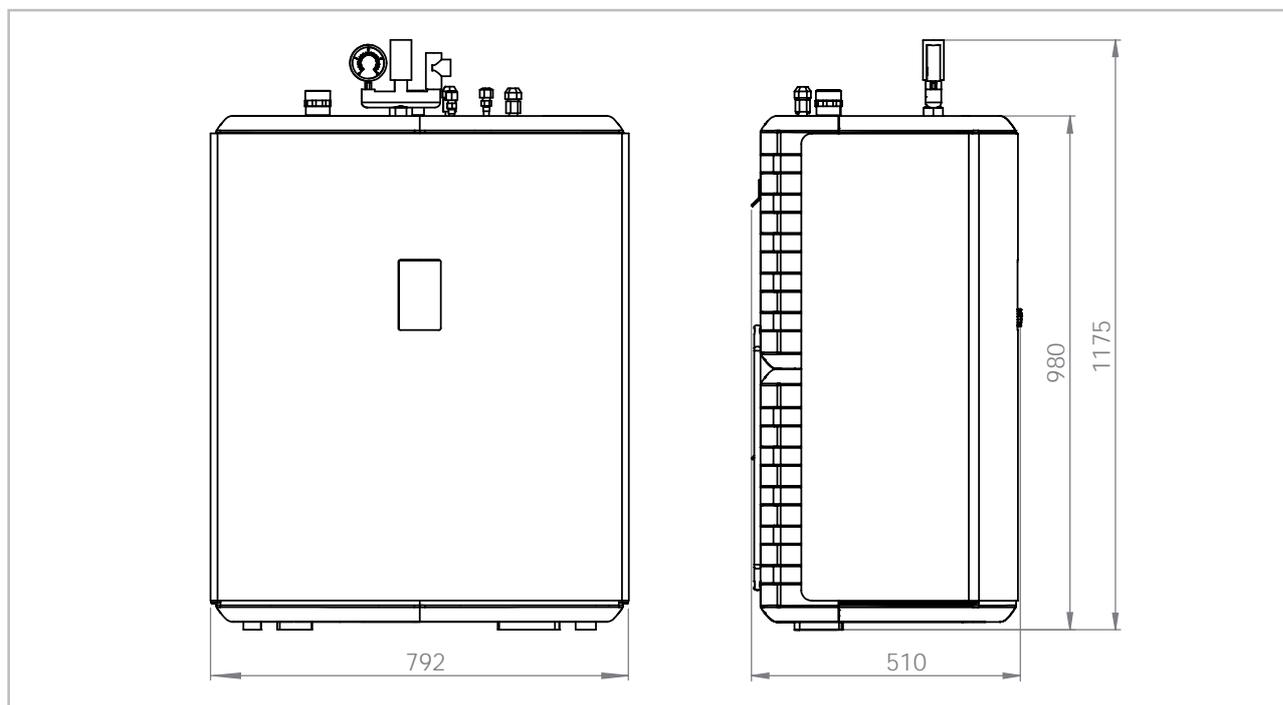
Dimensions du module interne série WKF 120/180 Duo (Toutes les dimensions en mm)
